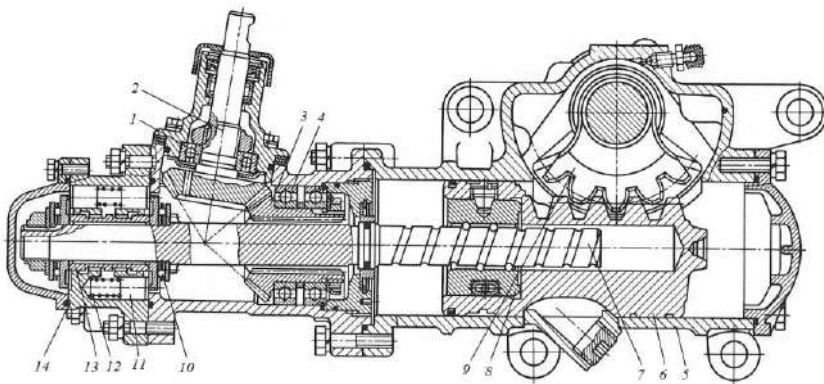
Рульовий механізм з шестеренним редуктором та передачею «гвинт – кулькова гайка – рейка – зубчастий сектор»:
